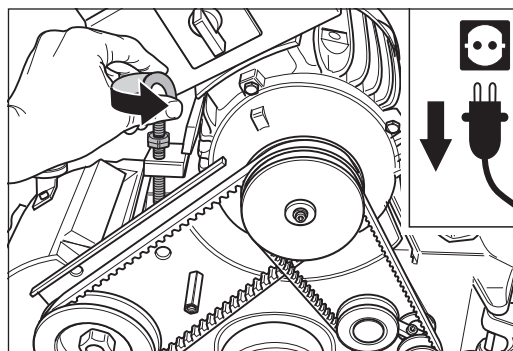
Die Ringschraube am Motor gegen den Uhrzeigersinn drehen.
